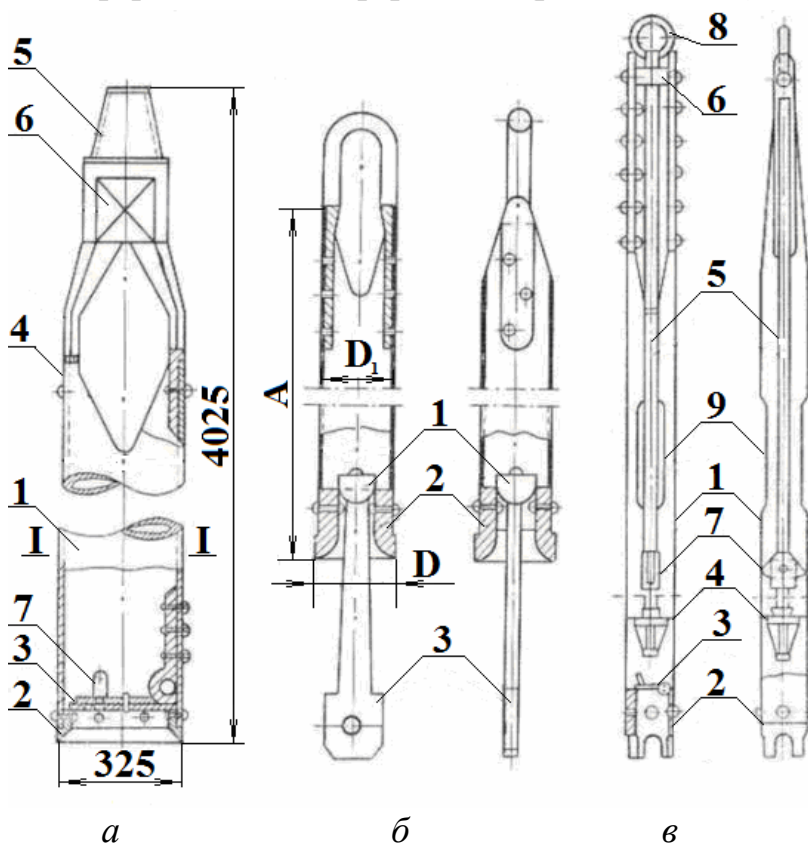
Схеми желонки: з плоским (а) клапаном, де 1 – корпус; 2 – башмак; 3 – клапан; 4 – дужка; 5 – конусна різь; 6 – шийка з ключовою виїмкою та напівсферичним (б) де 1 – клапан; 2 – башмак; 3 – язик, а також поршнева (в)
